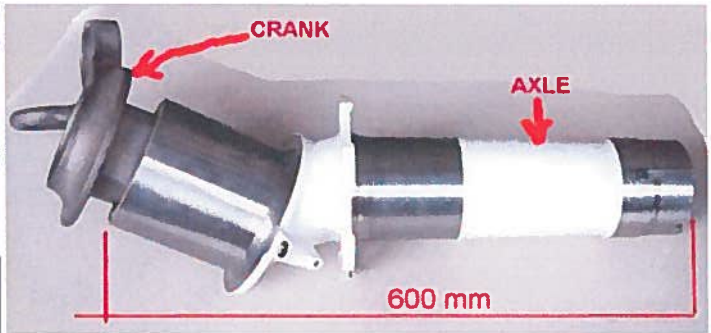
side brace lower - upper, rod end, bolt axle wheel MLG e crank semilavorati (mock-up)
